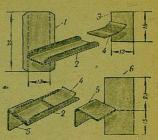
Направляющий желобок прерывателя трансмиттера: I — заготовка желобока, 2—желобок в согнутом виде, 3 — заготовка козырыка, 4 — козырек перед припайкой к желобку, 5 — угольник для крепления желобка к стойке, 6 — заготовка угольника.
